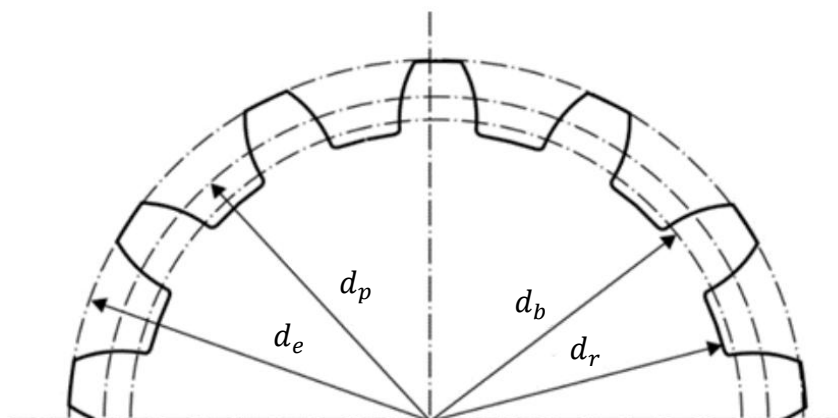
Diâmetros de uma engrenagem cilíndrica, [8].
